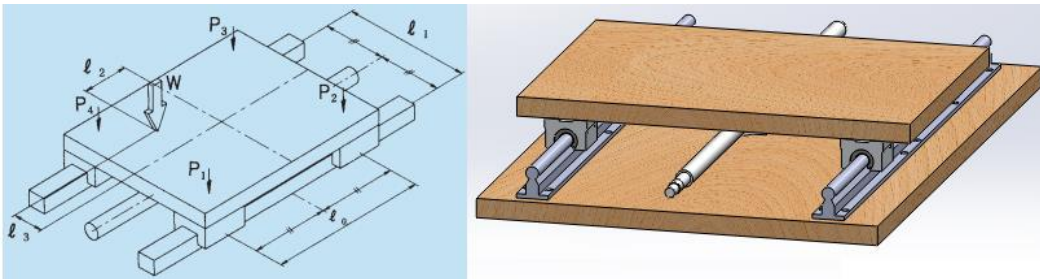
Parámetros que determinan las cargas del eje “Z”
